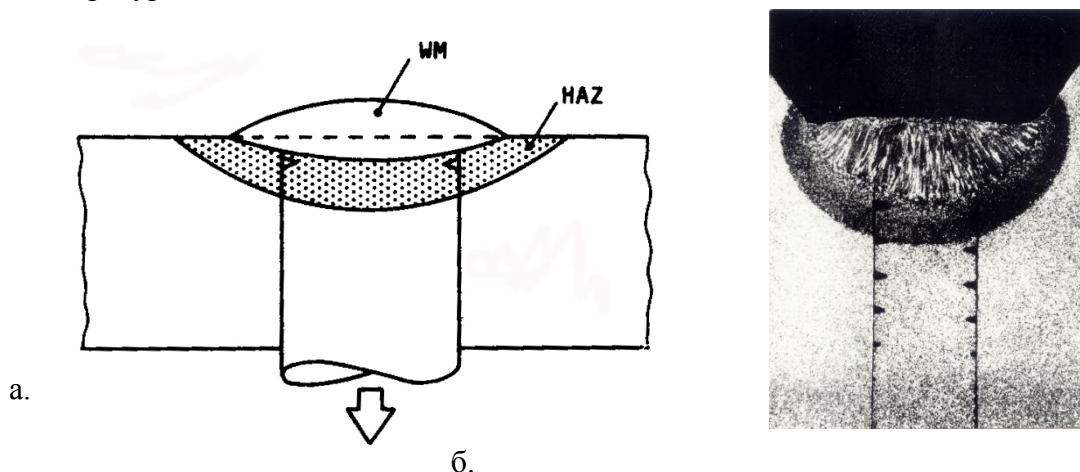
а. Схема нагружения образца «Имплант», где WM – металл шва, HAZ – зона термического влияния, стрелка – направления приложения нагрузки. б. Поперечный шлиф образца «Имплант» при наложении сварного валика на Y – образную разделку.
